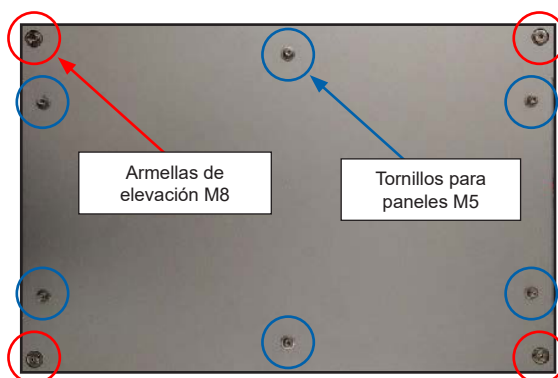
Puntos de fijación para armellas de elevación M8, vista del panel superior
